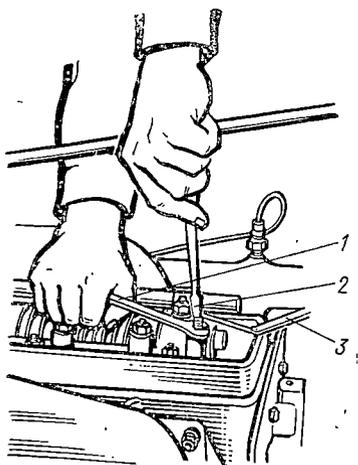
Регулировка зазора между стержнем клапана и бойком коромысла двигателя СМД-14:
